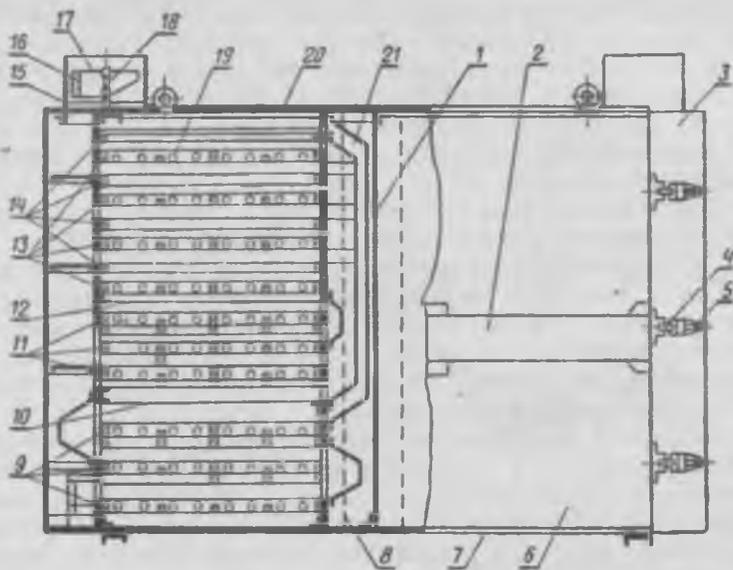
Ситовой корпус сепаратора А1-ЗСШ-20:
